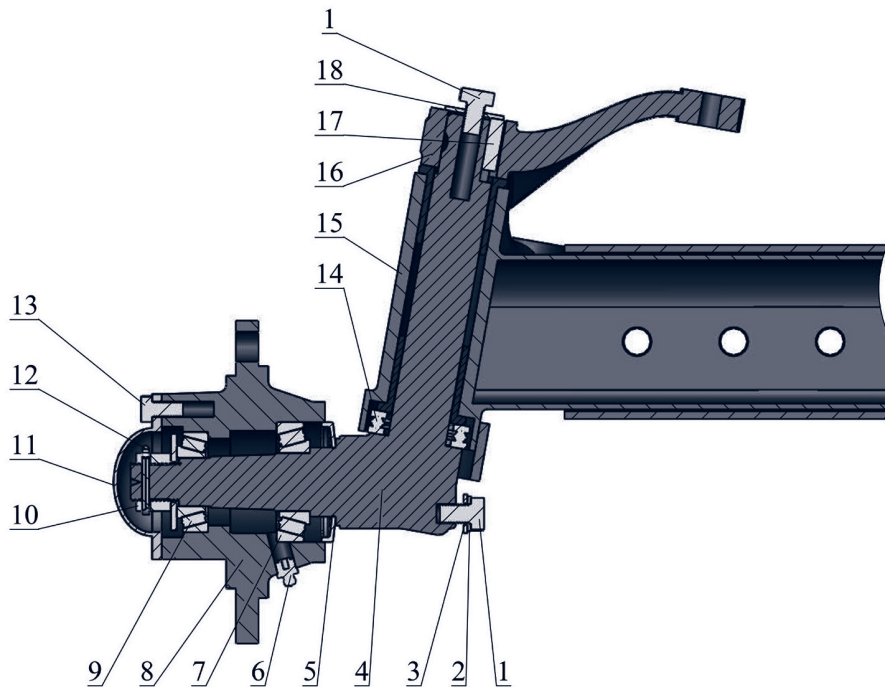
Регулировка зазоров колеи конических роликовых подшипников.
